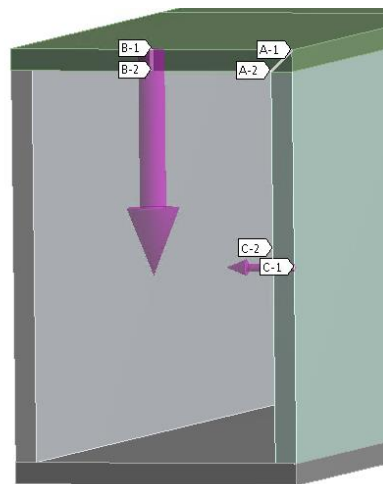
Localización de las SCLs A, B y C de la soldadura.
